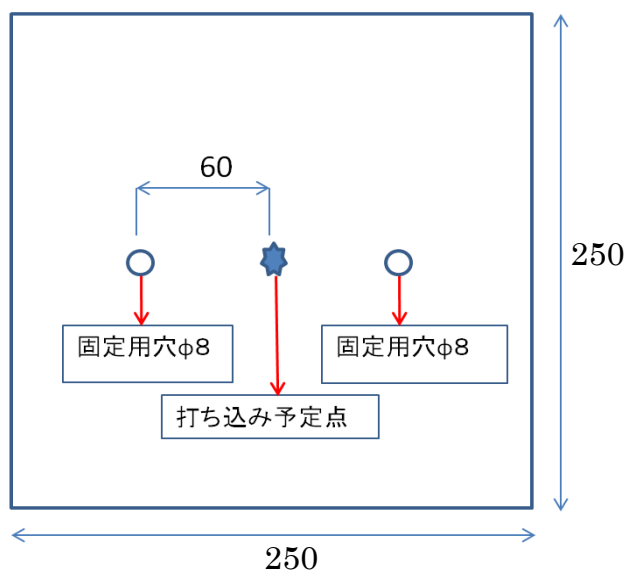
引き抜き試験の供試体の概要図 (単位 : mm)
